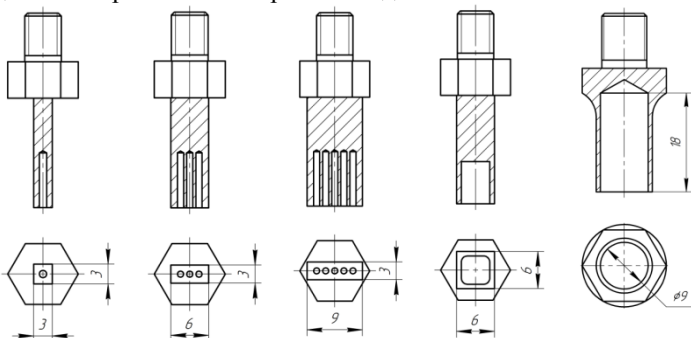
Пассивные рабочие инструменты для размерной обработки отверстий сложной формы
